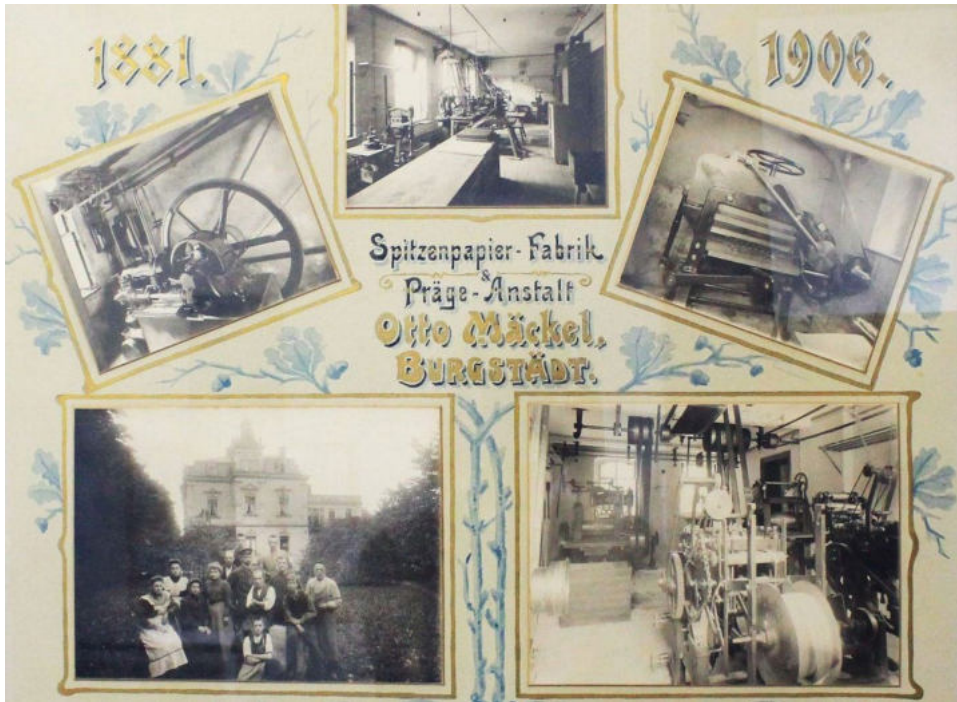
Jubiläumspakat der Spitzpapier-Fabrik und Prägeanstalt Otto Mäckel Burgstädt (Spitzenpapier-Fabrik und Prägeanstalt Otto Mäckel Burgstädt, Foto: C. Nehr Korn-Stege).
